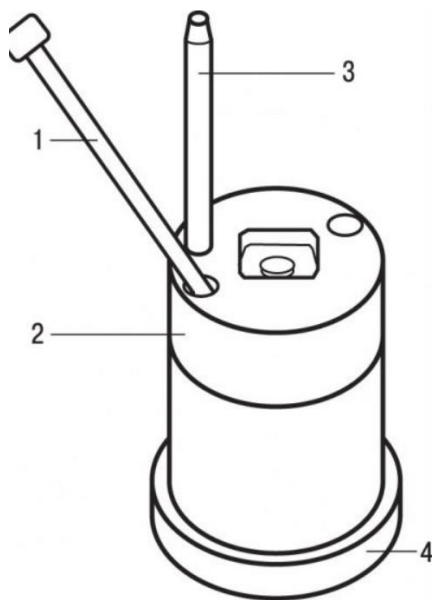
Положення пристроїв на опорному кронштейні балки задньої підвіски для випресування шарніра: 1 - болт тяги 0543-С; 2 - конус для випресування 0543-Е; 3 - напрямний елемент/опора 0543-В
